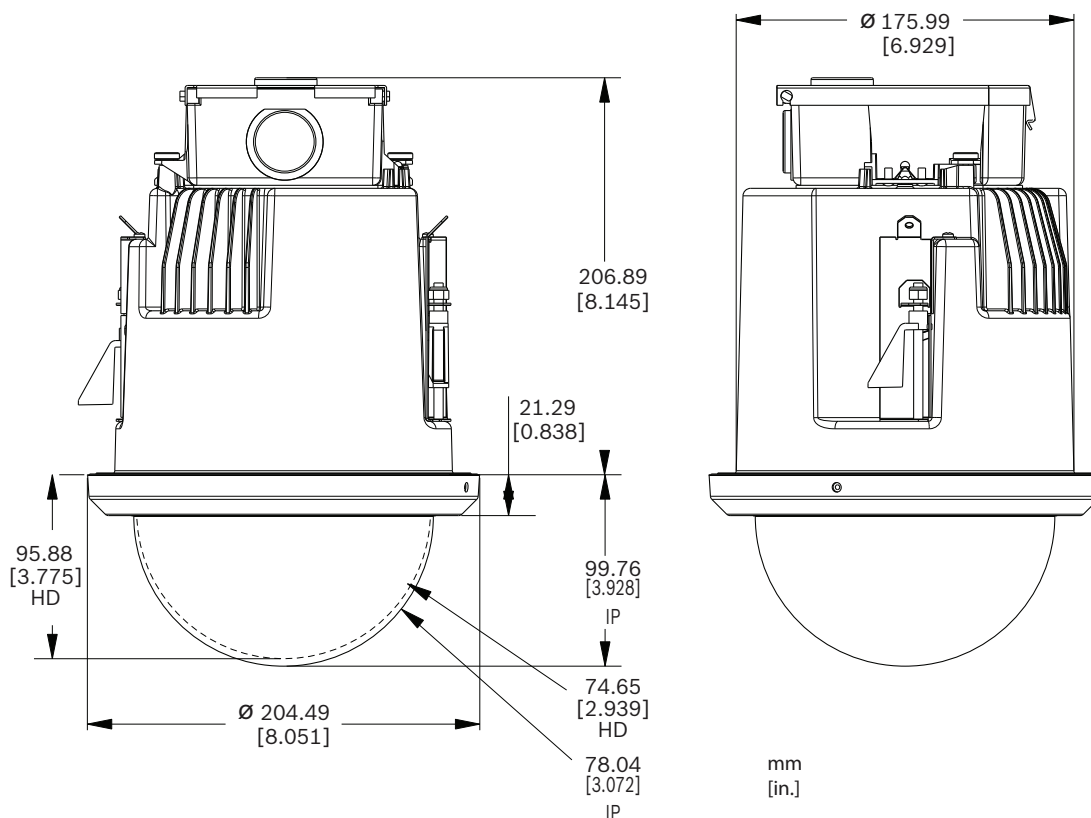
Dimensions de l'AUTODOME 7000 – encastrée au plafond
